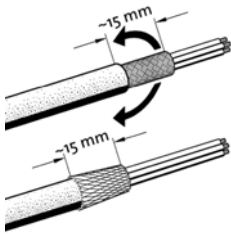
Auflegen von Kabelschirmen auf die EMV-Kabelverschraubungen (SC...FC WM
